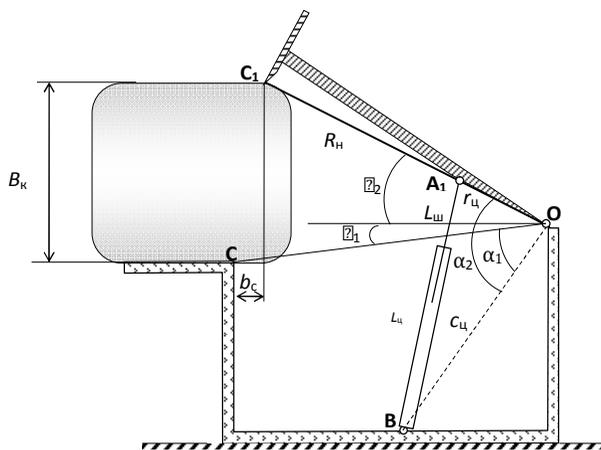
Кинематическая схема рычажно-консольного гидравлического ножа, режущая пластина в верхнем положении
